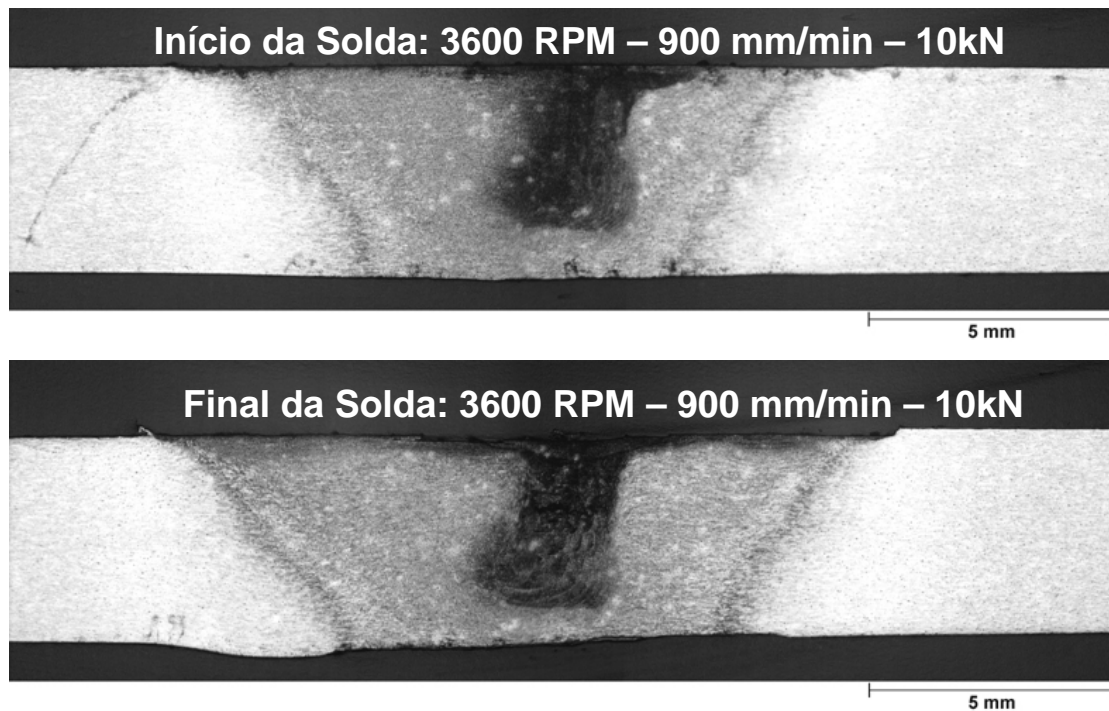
Macrografias das soldas FSW na liga 6013-T6 no início e final do cordão utilizando *backing* cerâmico, parâmetros de soldagem: velocidade de rotação de 3600 RPM, velocidade de avanço de 900 mm/min e força axial de 10 kN
